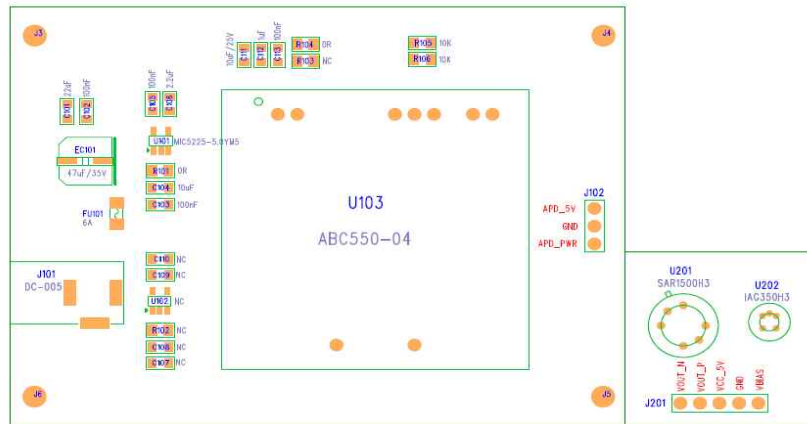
전원모듈 및 APD 연결용 pcb 설계도
